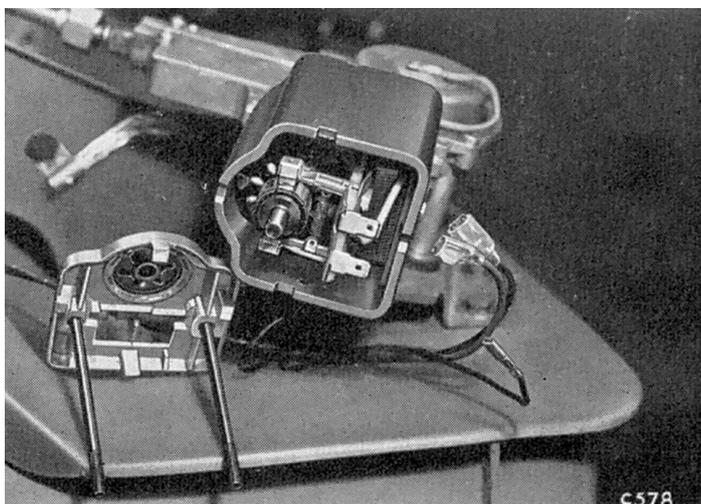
Couvercle d'extrémité enlevé pour montrer le mécanisme des balais
